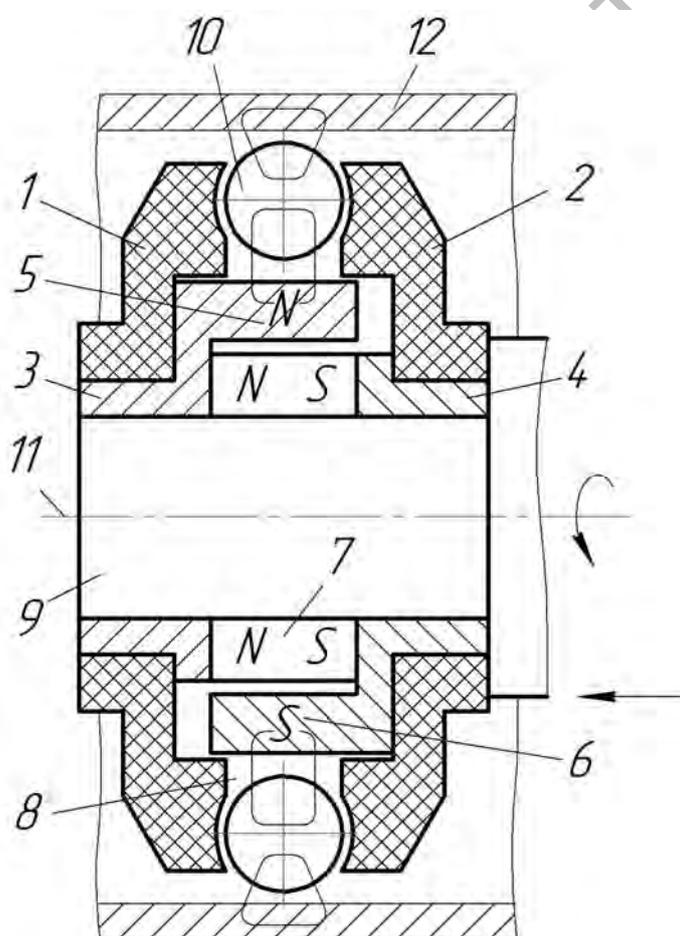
Конструкция инструмента с магнитной системой на основе кольцевого постоянного магнита, обеспечивающей перемагничивание деформирующих шаров и упрочняемой поверхности заготовки
